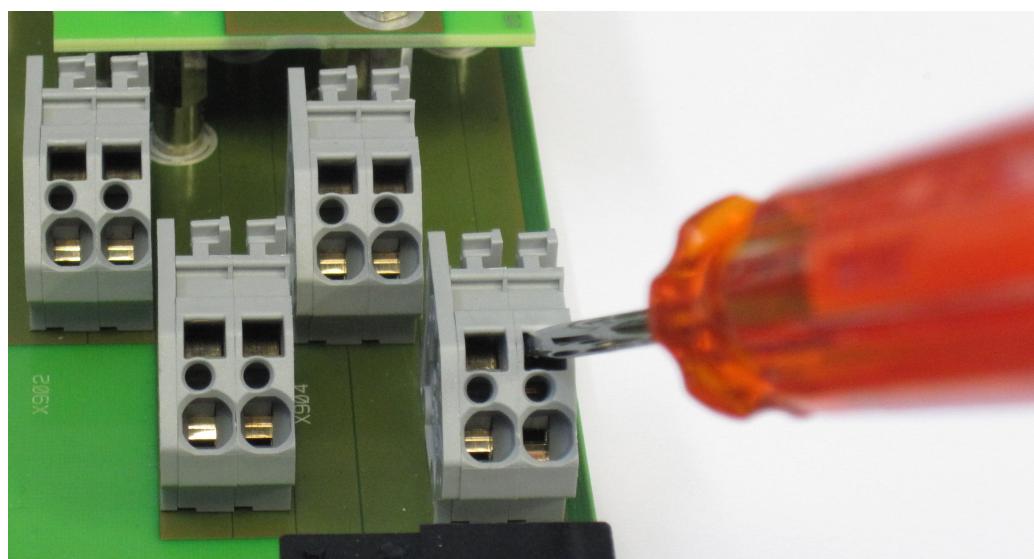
Der Draht kann in die untere runde Öffnung montiert werden
